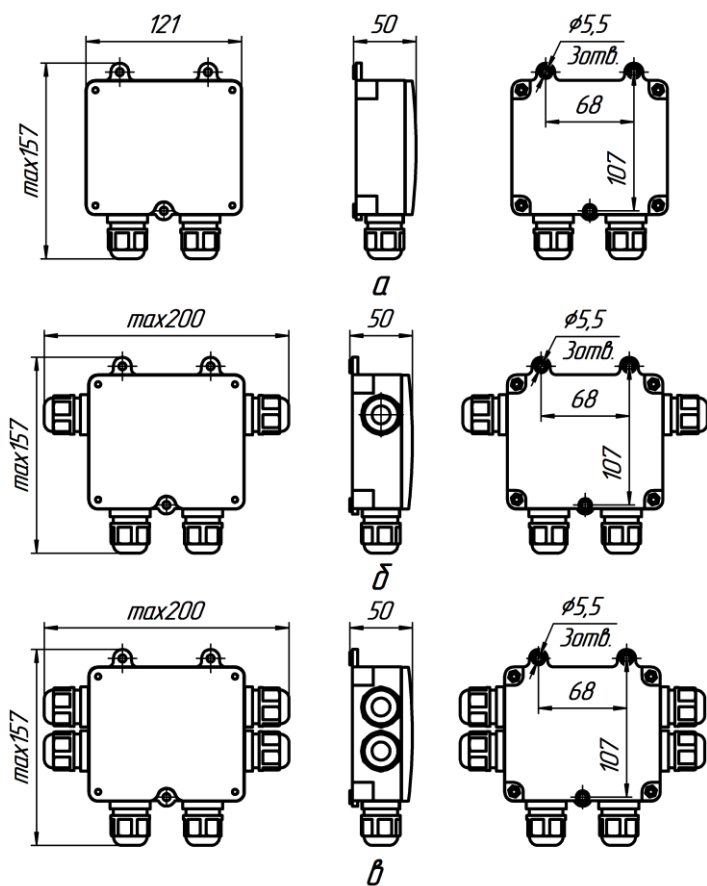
Установочные и габаритные размеры коробки соединительной.
